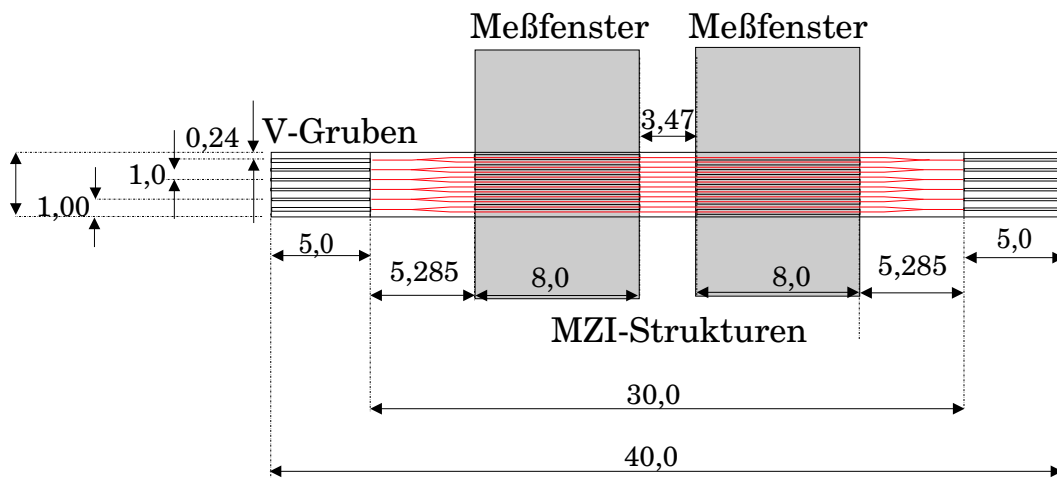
Dimensionierungen eines Mach-Zehnder Interferometer Chips (in mm).
